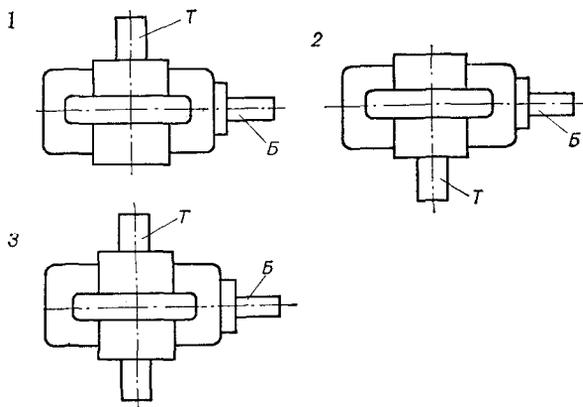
Схемы сборок (1—3) редукторов РЧН и РЧП:
